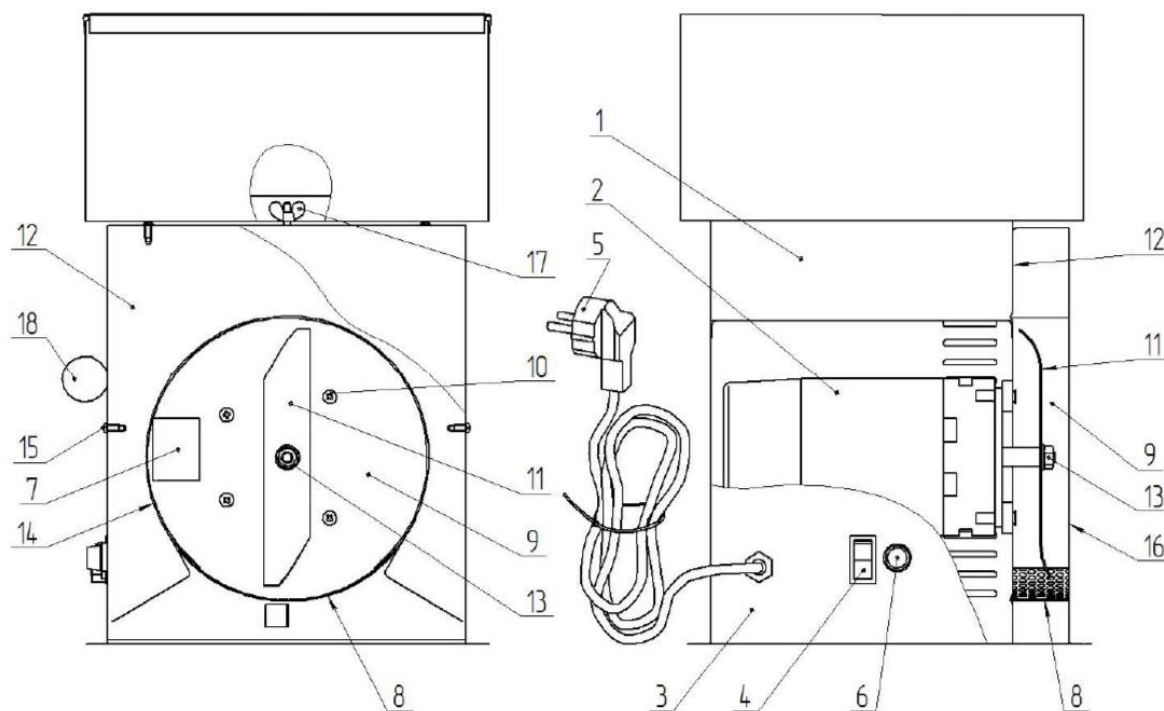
Устройство измельчителя зерна ИЗ-15 «Нива»: 1 – загрузочная камера; 2 – электродвигатель; 3 – корпус; 4 – переключатель клавишный; 5 – шнур сетевой; 6 – держатель предохранителя; 7 – подающее окно; 8 – сито; 9 – камера измельчения; 10 – крепежный винт; 11 – нож; 12 – основание; 13 – гайка; 14 – отражатель; 15 – винт-саморез; 16 – крышка передняя; 17 – гайка-барашек; 18 – заслонка подающего окна
